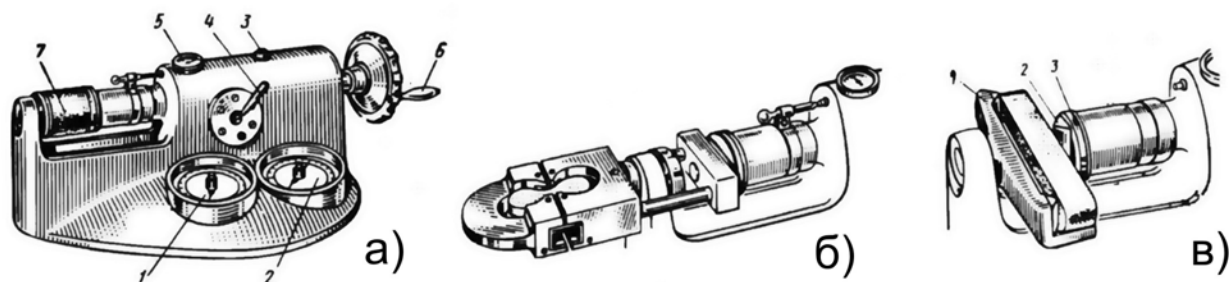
Универсальный прибор для испытания смесей на прочность на сжатие (а), дополнительное приспособление для испытания на разрыв (б), дополнительное приспособление для испытания на изгиб (в)
